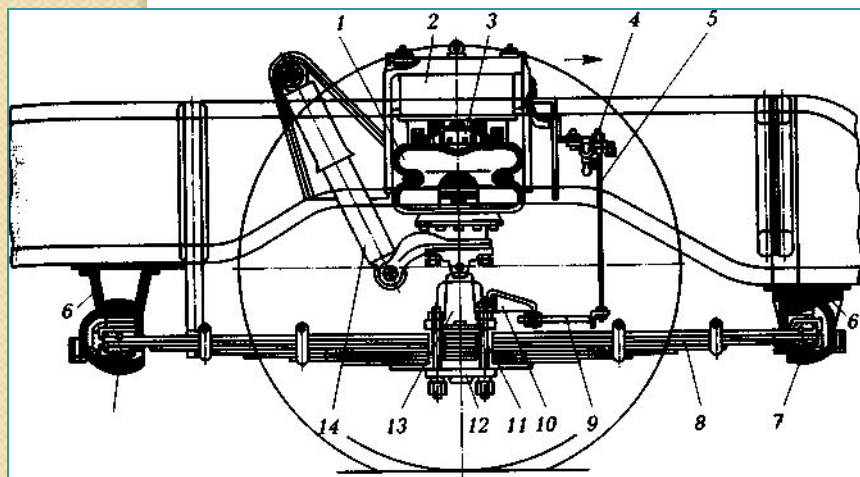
Передняя подвеска автобуса с пневмобаллонами и демфирующим устройством: 1 — пневмобаллоны; 2 — дополнительные резервуары; 3 — демфирующее устройство; 4 — регулятор; 5 и 9 — тяги; 6 — кронштейны балки; 7 — резиновая подушка; 8 — рессора; 10 — кронштейн; 11 — болт; 12 — накладка; 13 — балка; 14 — амортизатор; 15 — чашка
